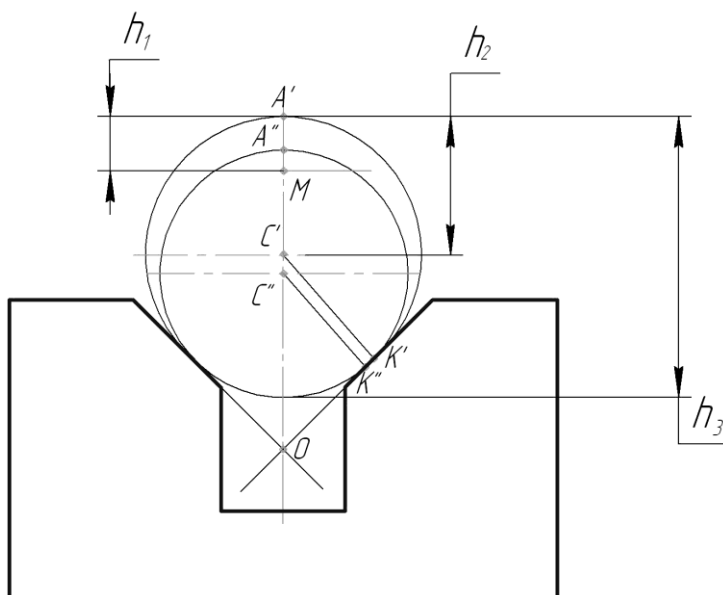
Пример базирования *наружными цилиндрическими* поверхностями.
